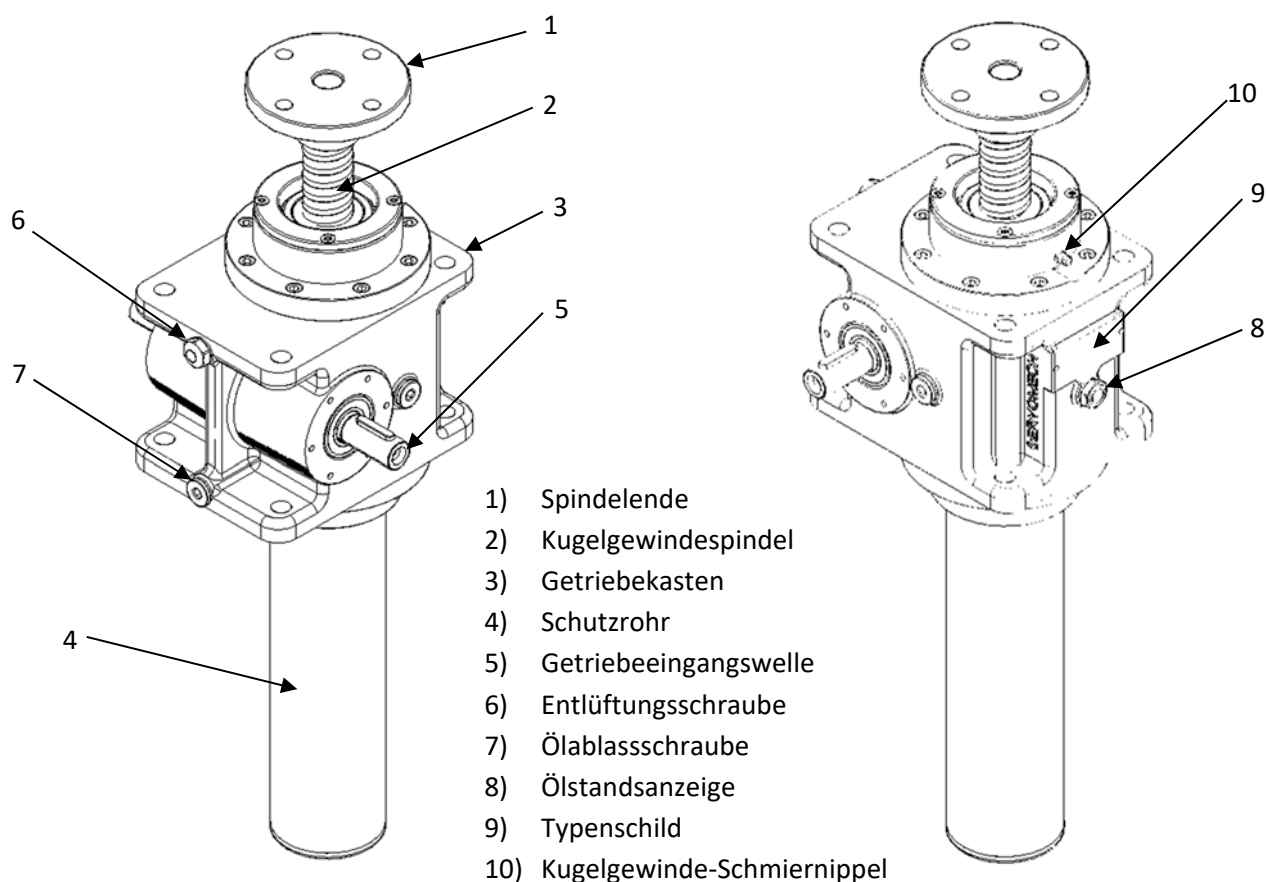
Hauptkomponenten des Kugelgewinde-Hubgetriebes:
